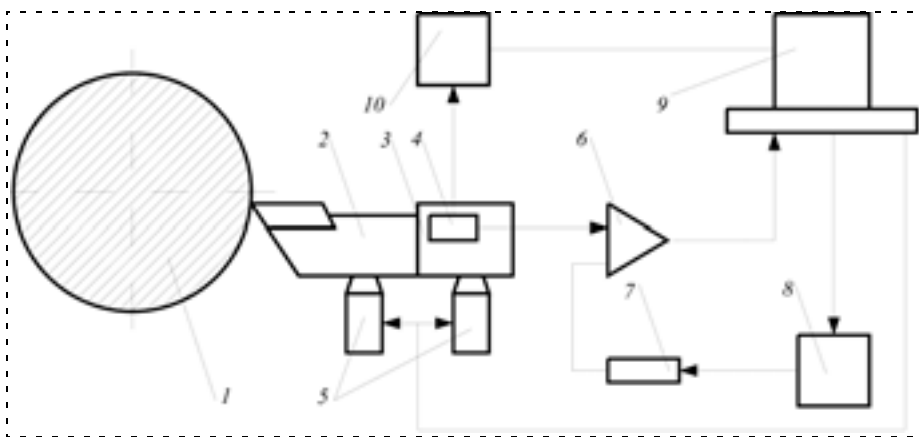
АСУ точностью обработки деталей на оборудовании с ЧПУ: 1 — деталь; 2 — резец; 3 — резцедержатель; 4 — силовой датчик; 5 — исполнительные механизмы с ЧПУ; 6 — операционный усилитель; 7 — резистор; 8 — контроллер; 9 — компьютер; 10 — аналого-цифровой преобразователь
